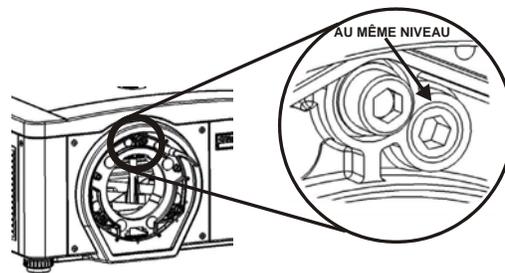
ALIGNEMENT DES VIS DE SERRAGE
